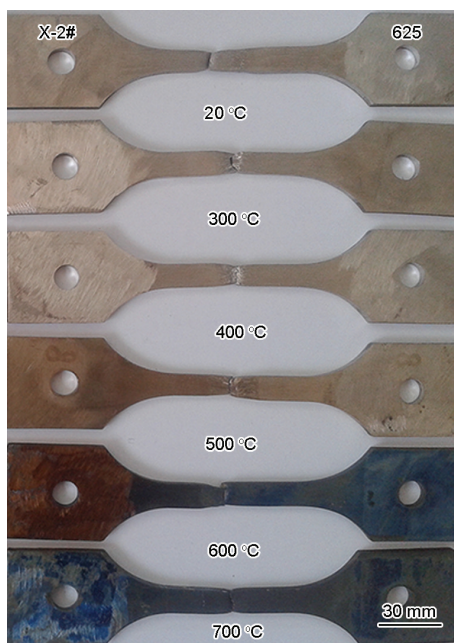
X-2#/625 异种金属焊接接头在不同温度进行拉伸实验后的宏观形貌
